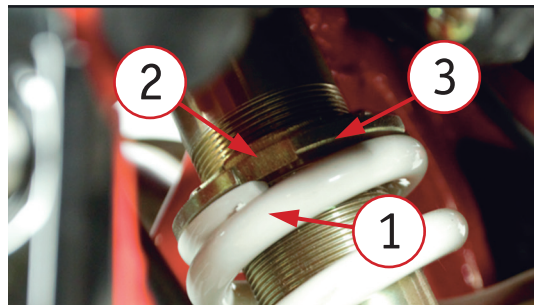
Регулировка преднатяга амортизатора: 1 – пружина; 2 – стопорная гайка, 3 – регулировочная гайка.
